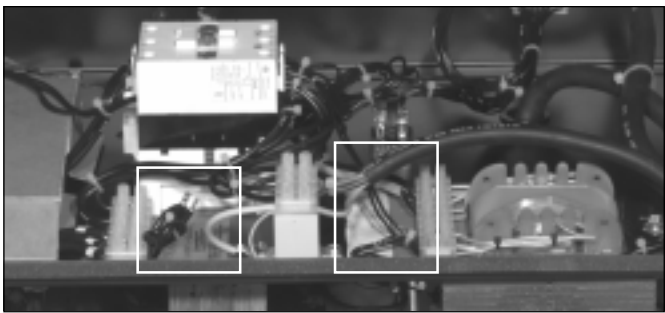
Tablette à bornes des transformateurs de soudage et de commande
